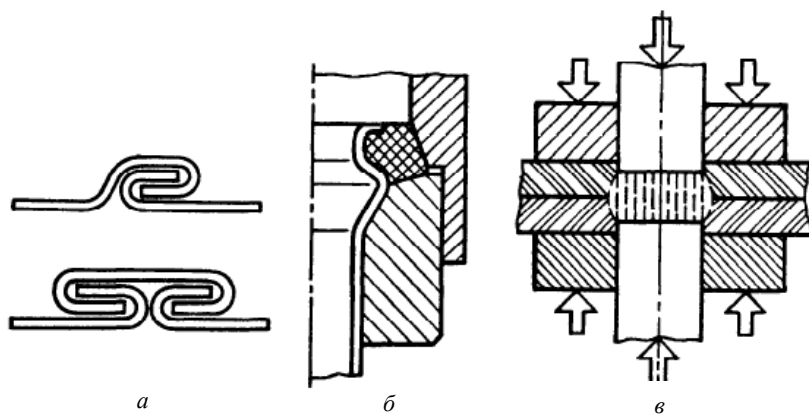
Схемы штамповборочных операций листовой штамповки, выполняемых: *a* – гибкой; *б* – раздачей; *в* – холодной сваркой
